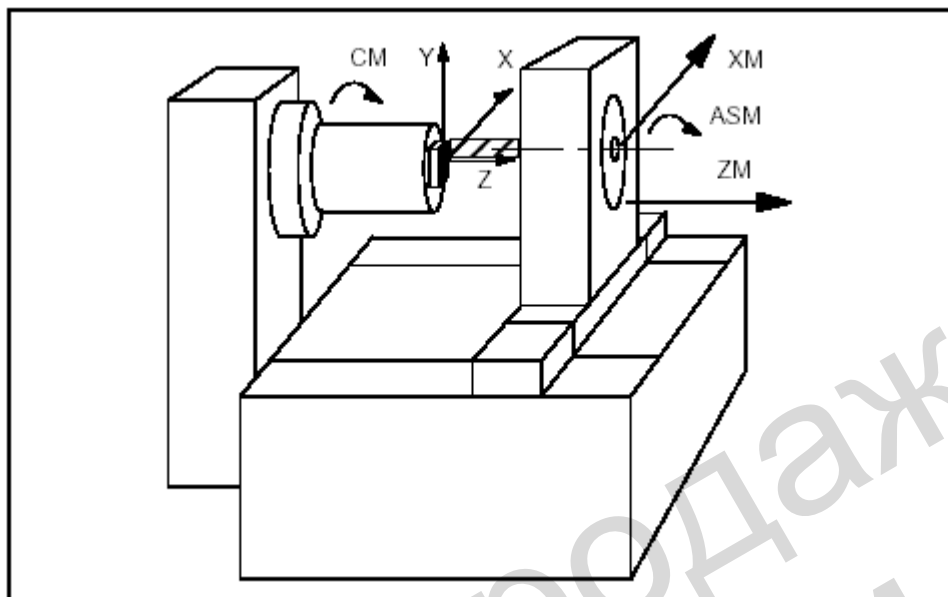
Торцевая фрезерная обработка обрабатываемой детали с помощью TRANSMIT
